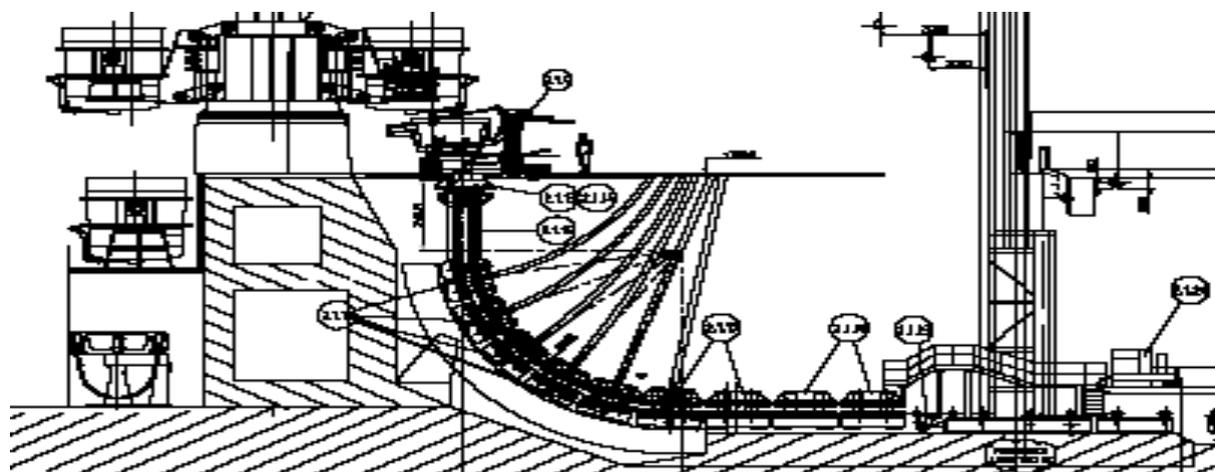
Устройство для приема сталь-ковша и поворотный стенд
